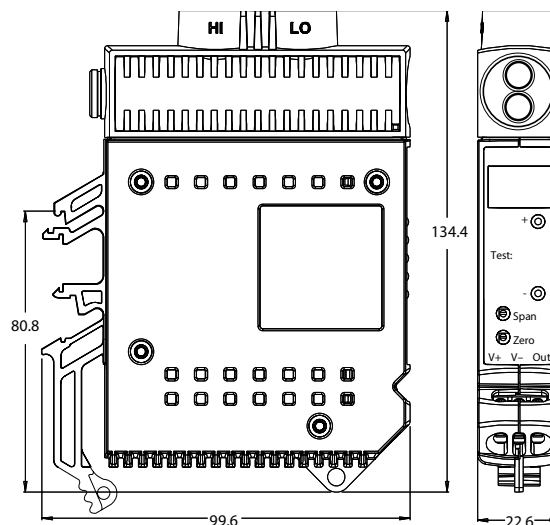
Dimensions avec la vanne de sélection et les vis de réglages (en mm)
